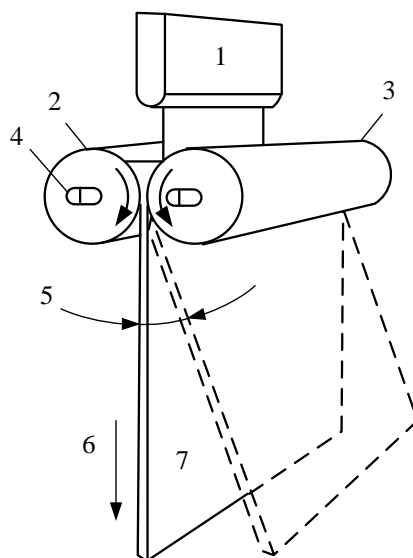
Схема кристаллизатора двухвалковой установки для отливки полосы: 1 – щелевое разливочное устройство; 2 – первый валок; 3 – второй валок; 4 – удельное давление металла на валки; 5 – угол отклонения полосы; 6 – направление разливки; 7 – быстро затвердевшая полоса
